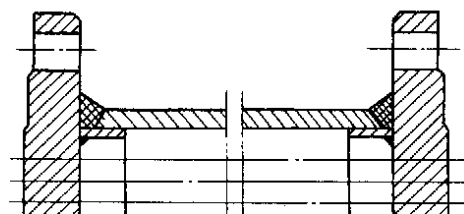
$DN < 600\text{mm}$ 时管板与壳体的焊接型式
